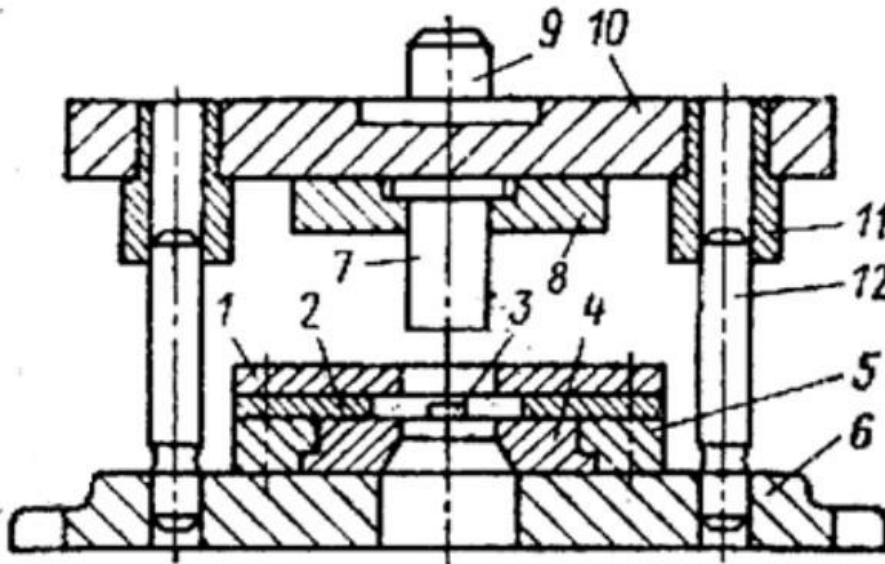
Схема вырубного штампа: 1 - съемник; 2 - направляющие линейки; 3 - уголок; 4 - матрица; 5 - матрицедержатель; 6, 10 - нижняя и верхняя плиты; 7 - пуансон; 8 - пуансонодержатель; 9 - элостовик; 11 - направляющие втулки; 12 - направляющие колонки
